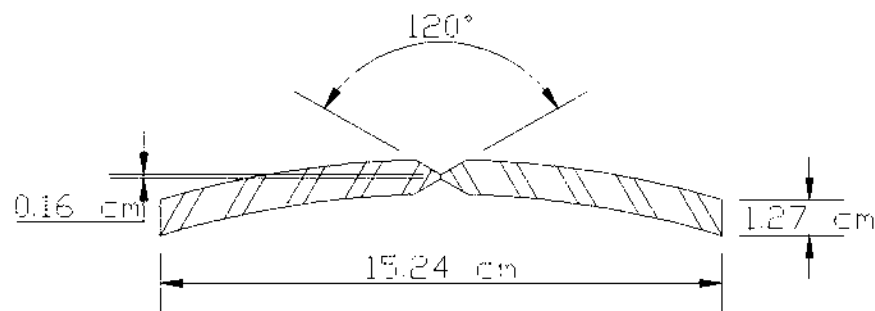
Diseño de junta utilizada para pruebas de soldadura con aplicación de campo magnético.
